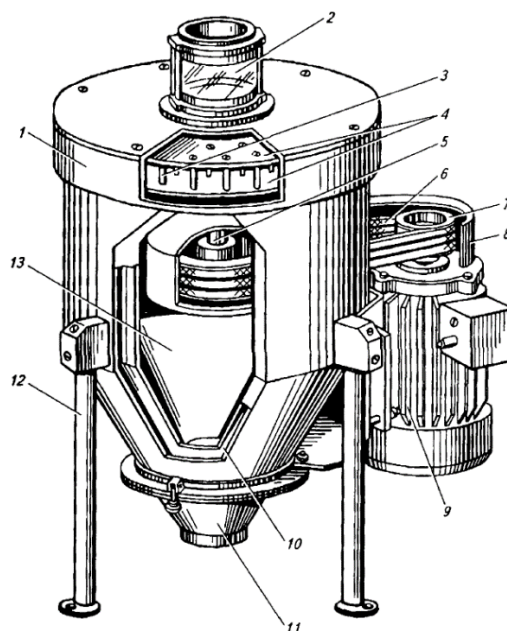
Энтолейтор РЗ-БЭЗ:
